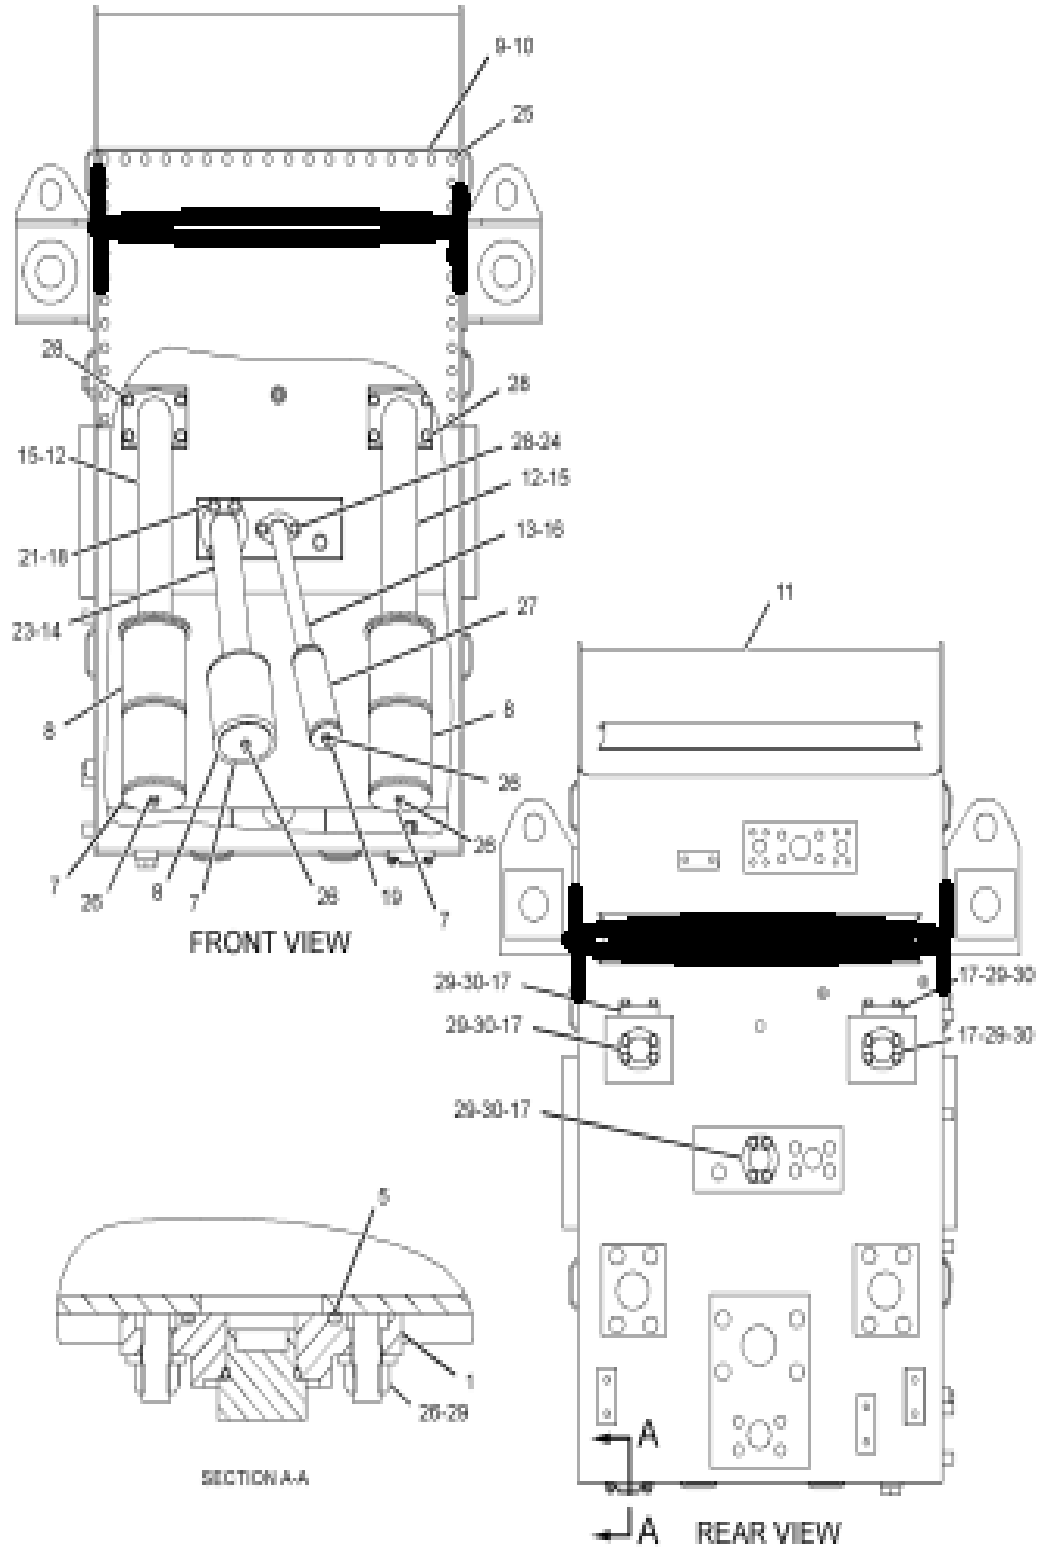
soudage d'une traverse avec les fixations du réservoir hydraulique
